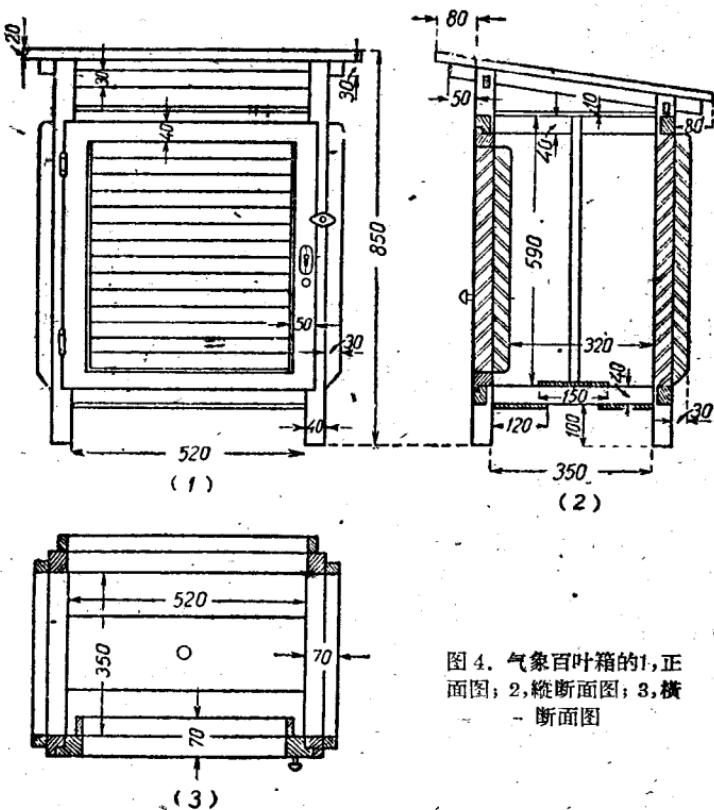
气象百叶箱的1.正面图; 2.纵断面图; 3.横断面图
